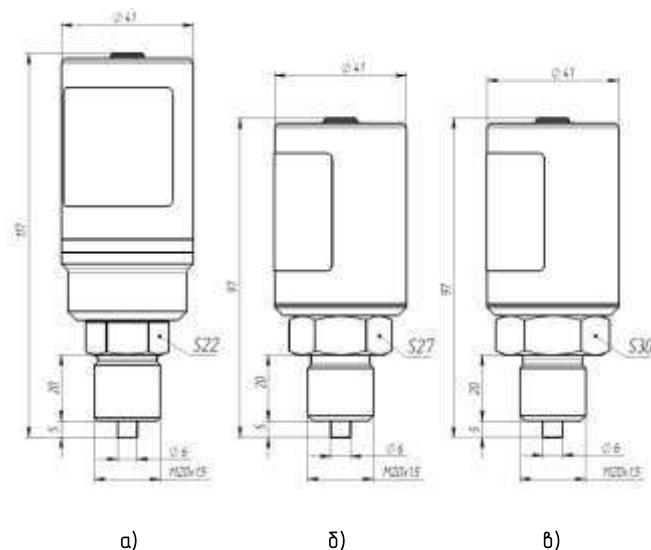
Габаритные размеры преобразователей давления конструктивных исполнений 1 и 2.
